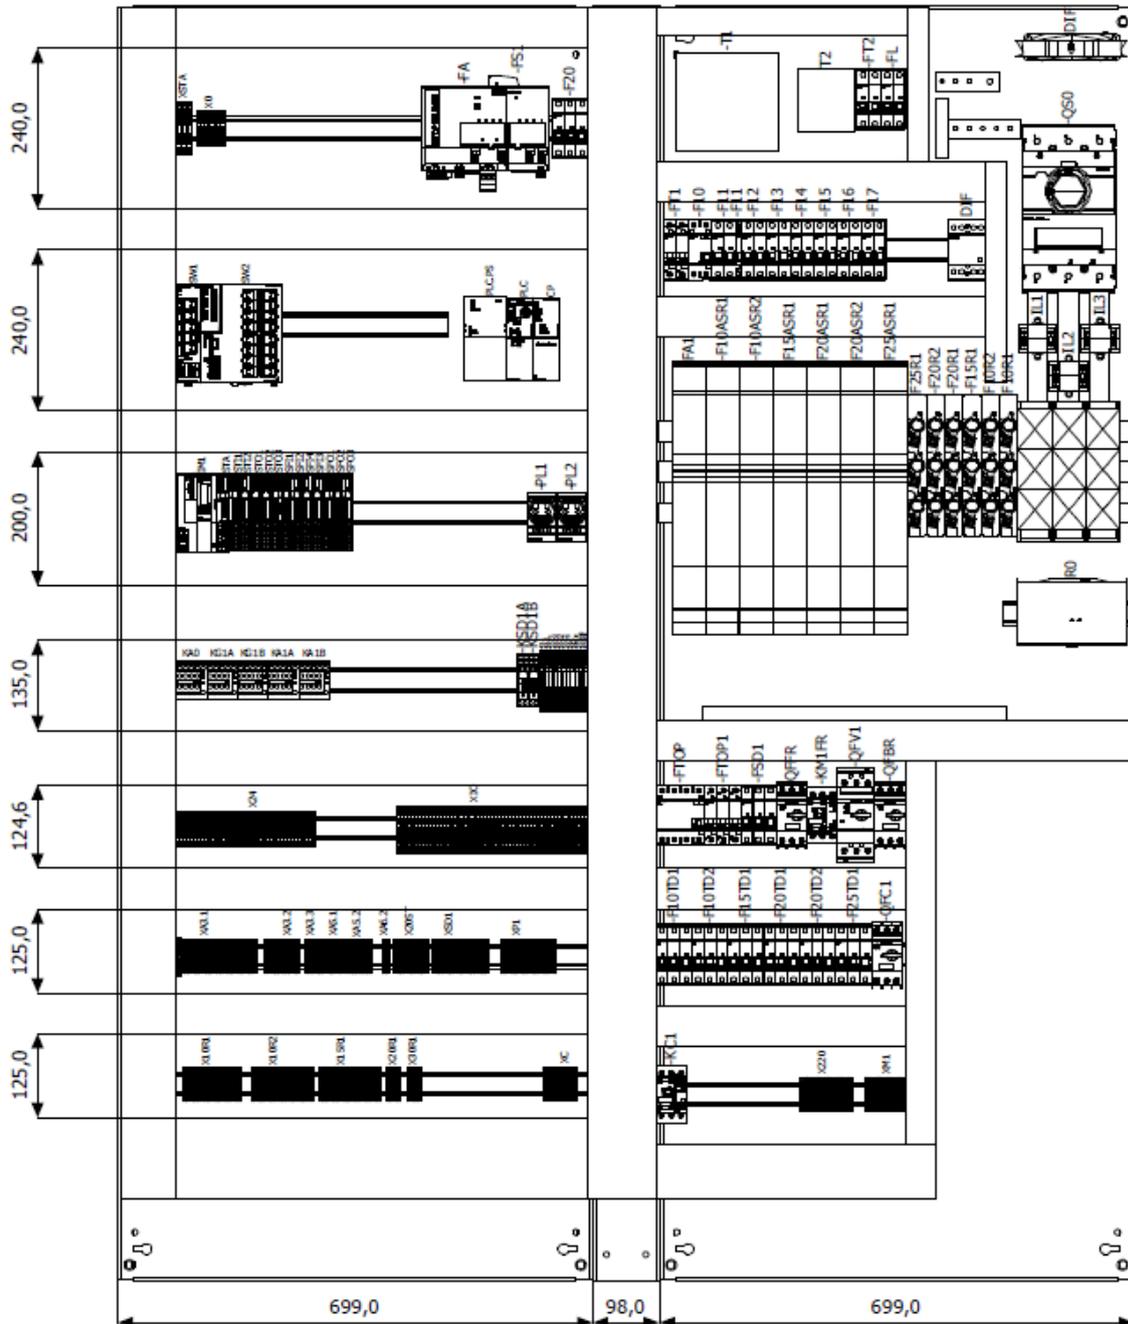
Imagen croquis interior del armario eléctrico.
